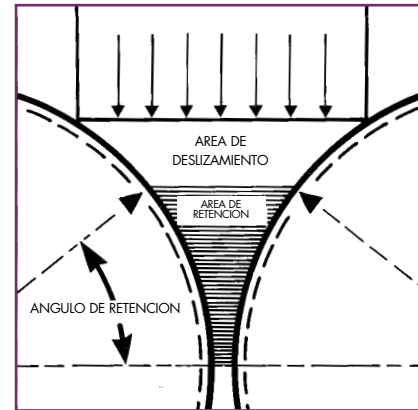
GEOMETRIA DE LA COMPRESION A RODILLOS
